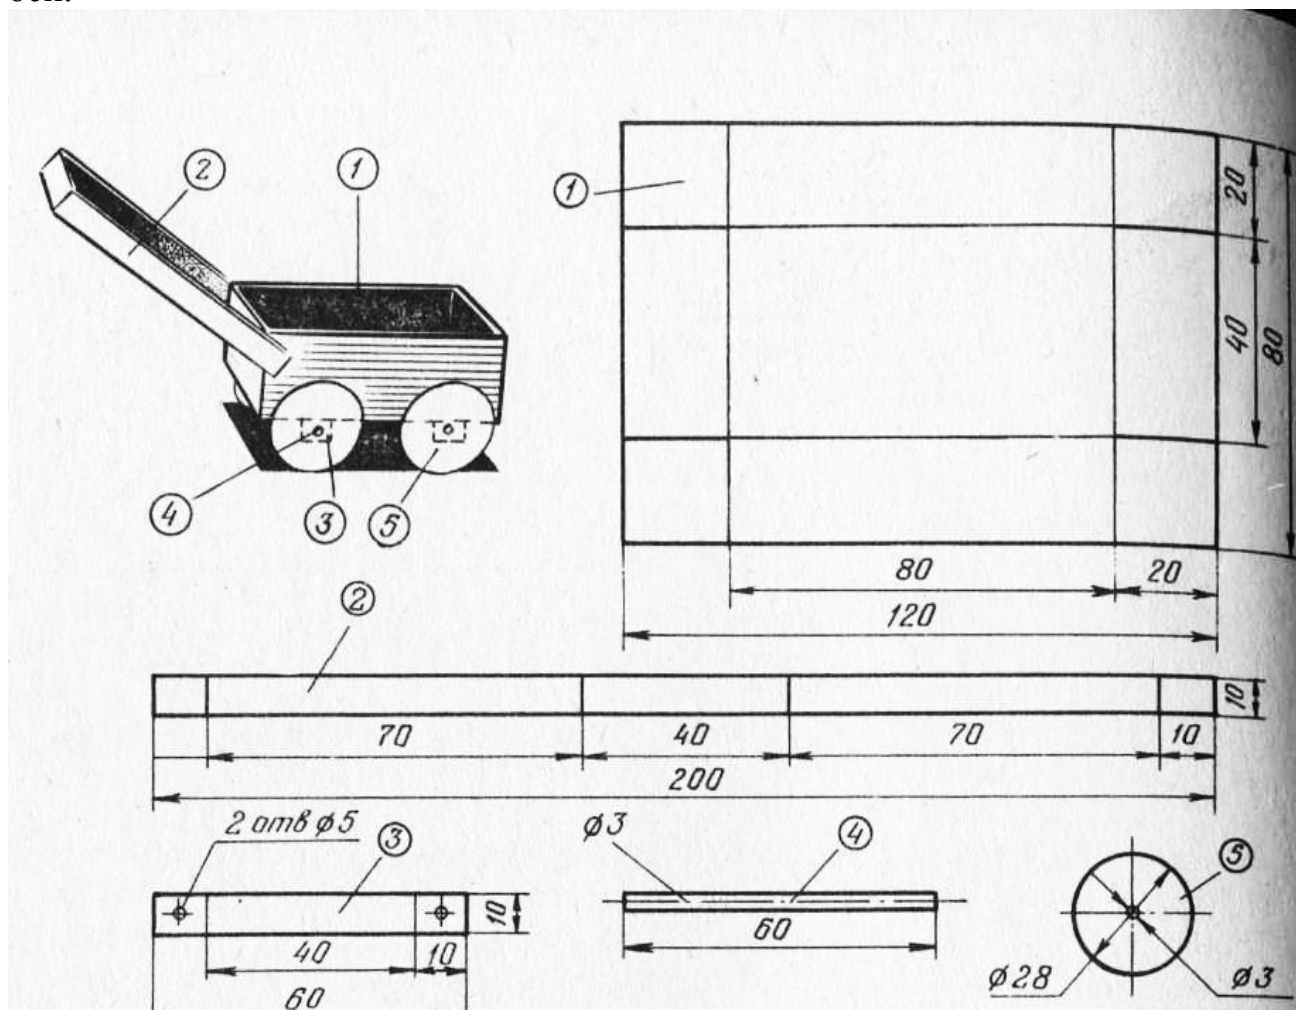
Модель тележки: 1— корпус; 2— ручка; 3— подшипник; 4— ось; 5— колесо
